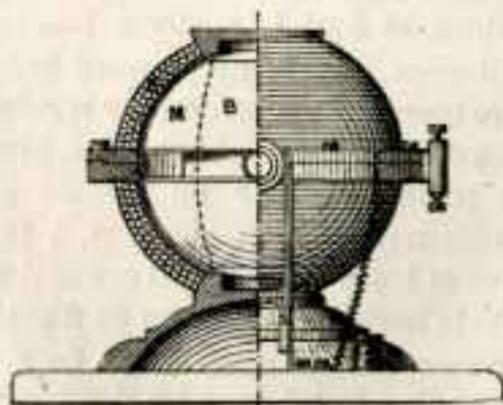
Moteur Burgin (vue de la sphère intérieure)
